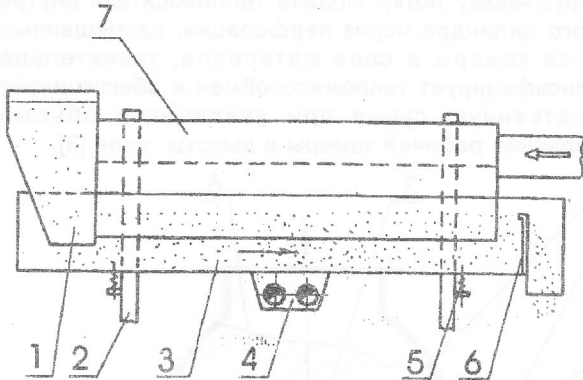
Горизонтальная лотковая вибросушилка с верхним расположением газоподводящего короба 1 - бункер; 2 - рама; 3 - виброток; 4 - вибратор; 5 - пружины; 6 - поворотная заслонка; 7 - газоподводящий короб.
